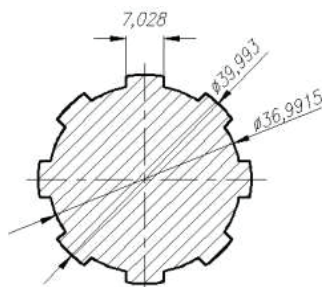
Эскиз калибра - пробки шлицевого прямобочного соединения $d-8\times 36H7 / f7\times 40H12 / a11\times 7D9 / h8$
